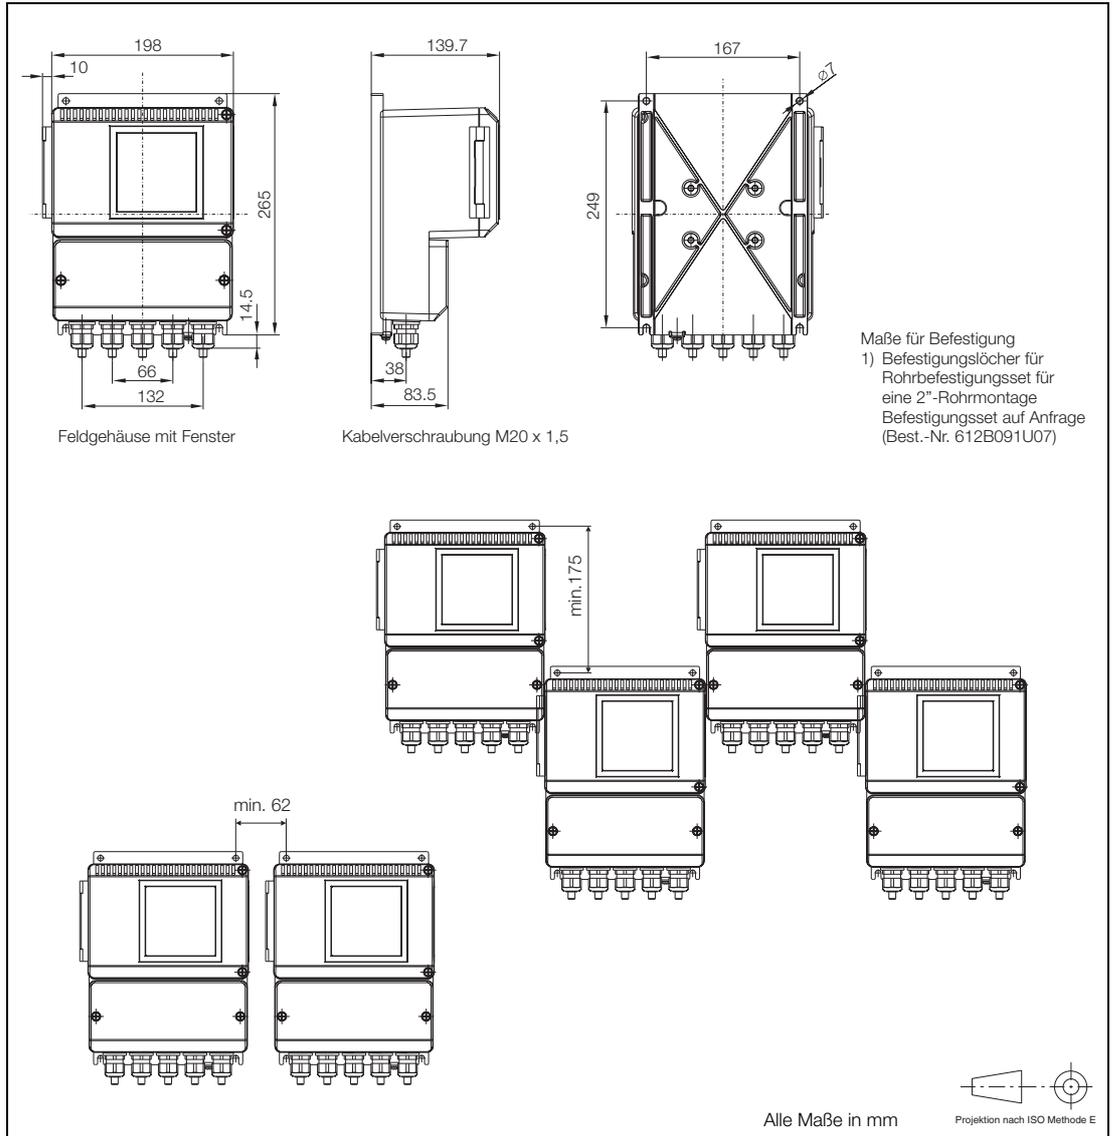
Maßzeichnung Messumformergehäuse im Montagevorschlag
